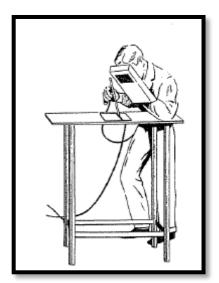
Posición del operador en la soldadura (Vidondo y Alvares, 1981, p.170).
